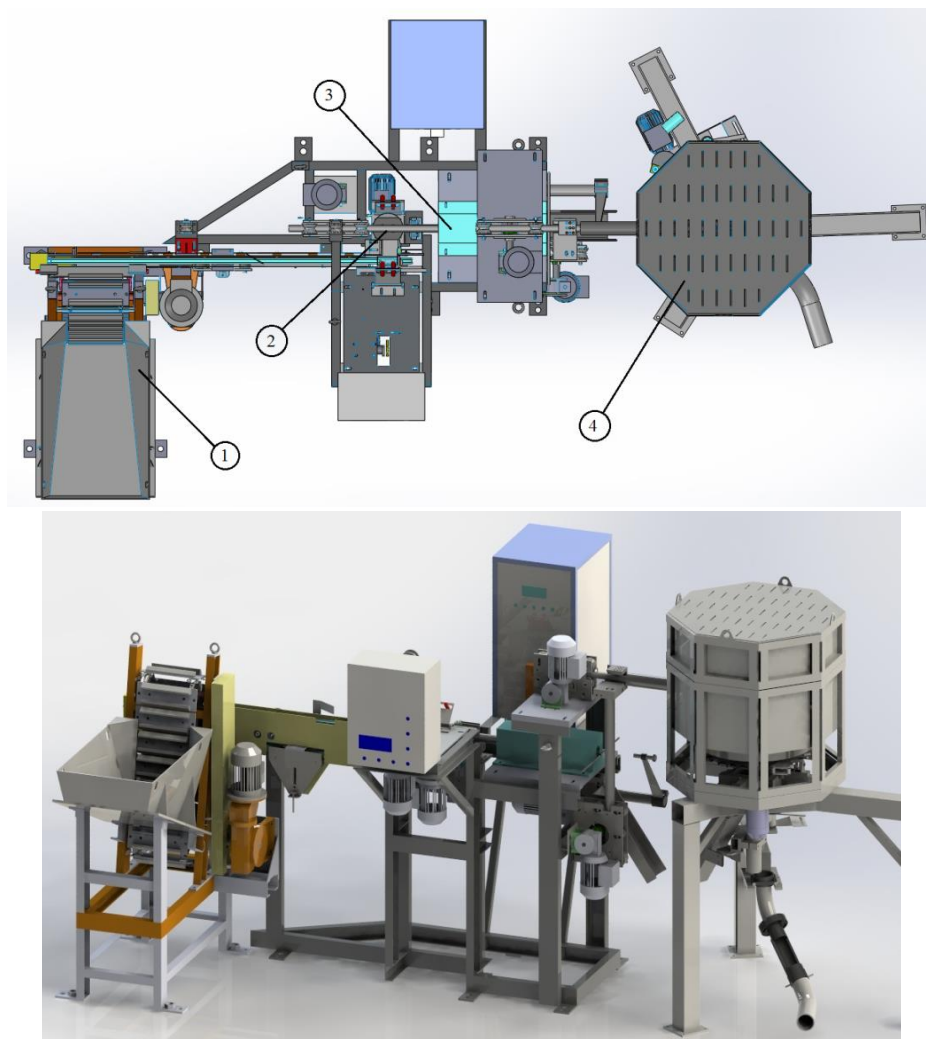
Нагревательное устройство штучных заготовок: 1 – загрузочный бункер;
